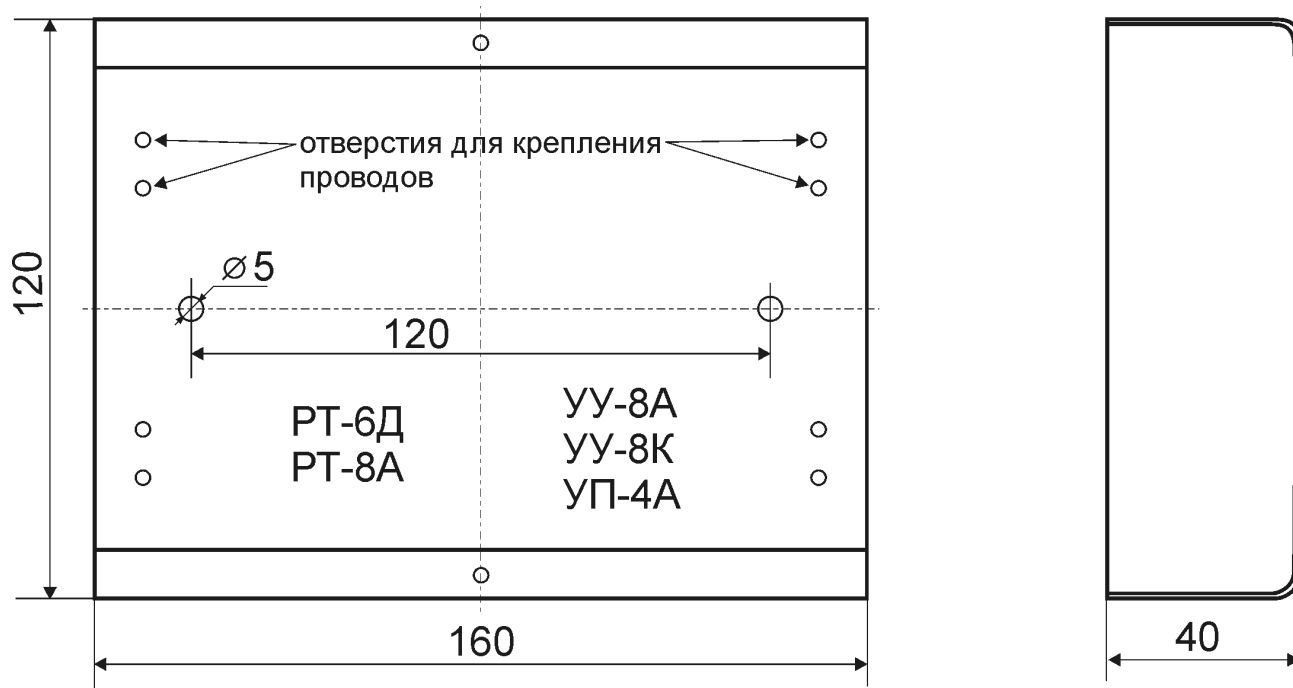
Габаритные и установочные размеры РТ-6Д, РТ-8А, УУ-8А, УУ-8К, УП-4А
